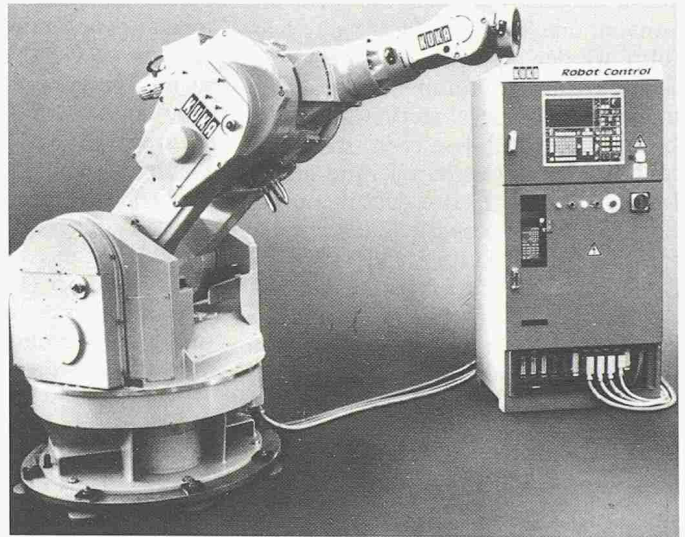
Industrieroboter für Montageaufgaben mit geringer Traglast, kinematisch gleich aufgebaut wie die grossen Punktschweiss-Roboter des gleichen Herstellers. Die zugehörige Siemens-Steuerung bietet Ein- und Ausgabekanäle und die Möglichkeit eines Sensoranschlusses. (Werkbild KUKA)
